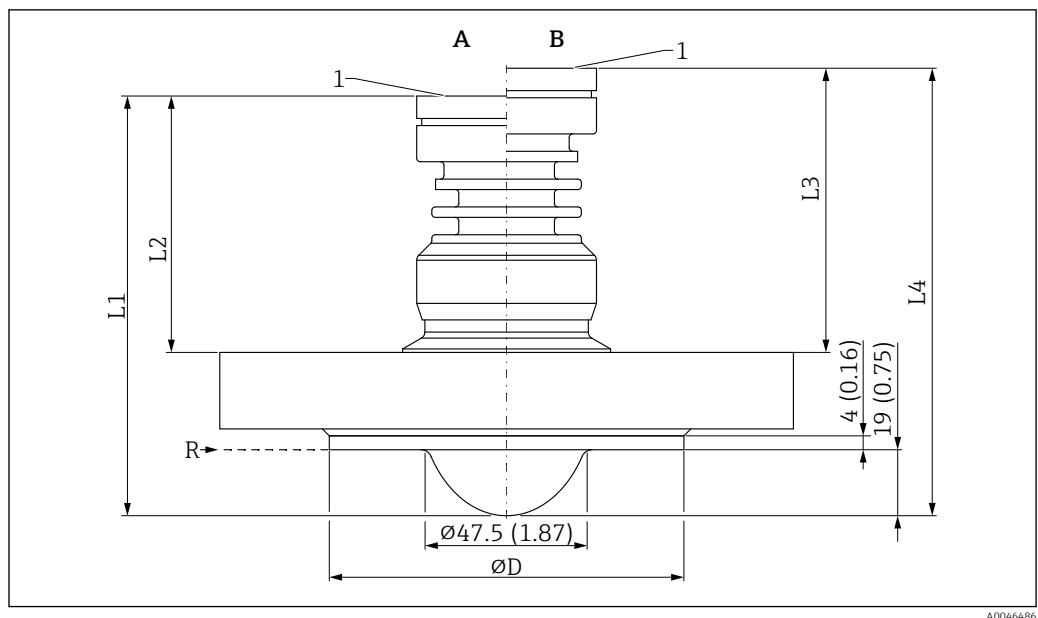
Dimensões da flange de conexão do processo. Unidade de medida mm (in)
